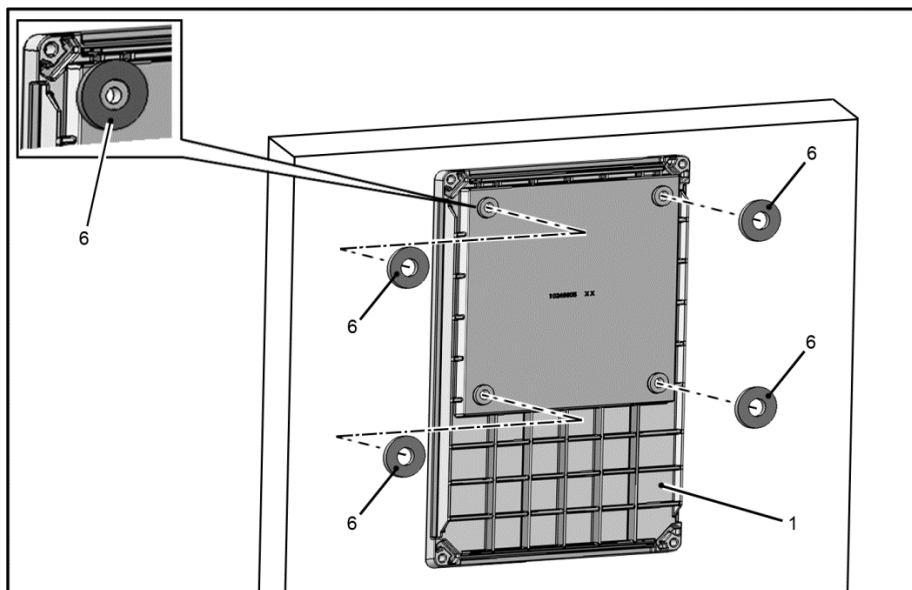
Aufsetzen Flachdichtungen auf Rückseite Adapterplatte
